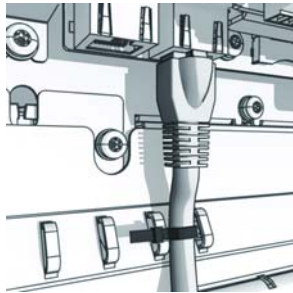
Befestigung der Kabel mit Kabelbindern
